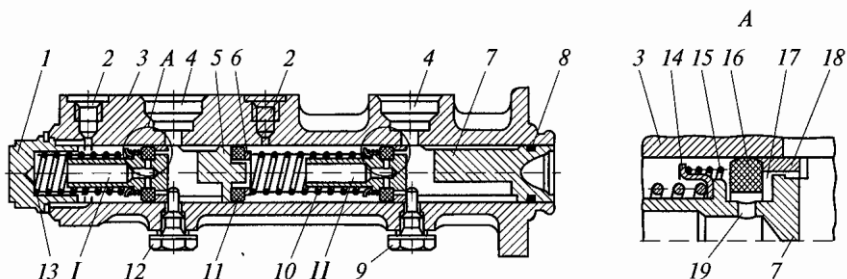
Главный тормозной цилиндр легковых автомобилей ВАЗ:
